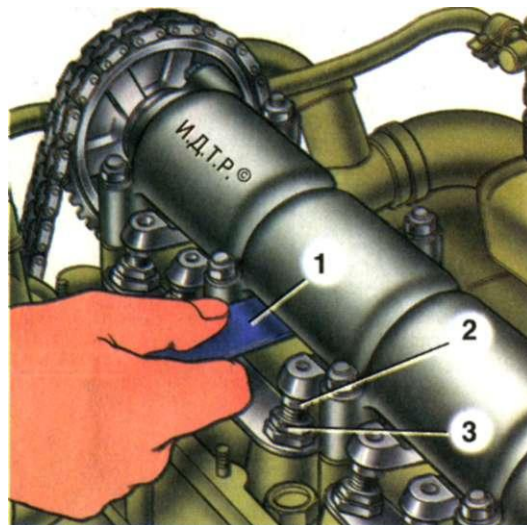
Проверка зазора между рычагами и кулачками распределительного вала: 1 - щуп; 2 - регулировочный болт; 3 - контргайка регулировочного болта.
